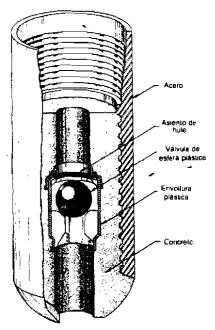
Detalles de un tapón de cementacion o zapata de flotación, con válvula de retención a bola, adecuado para trabajos en pozos.
